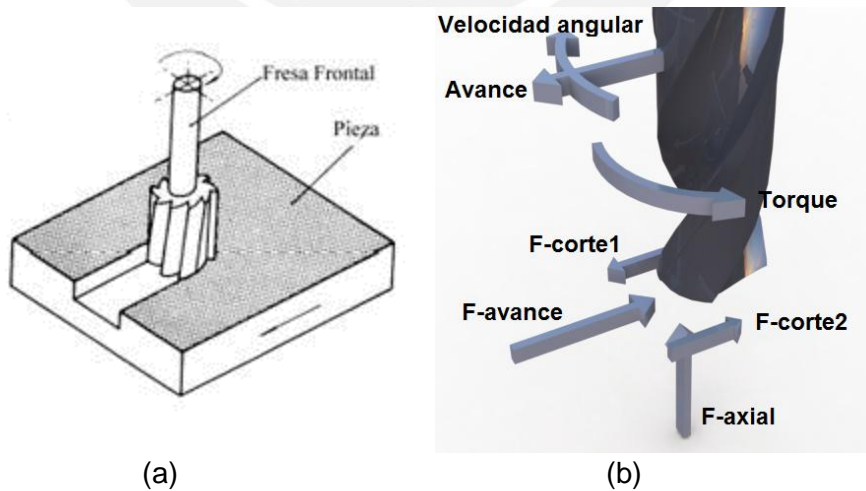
(a) Fresado frontal. (b) Descomposición de las fuerzas.
